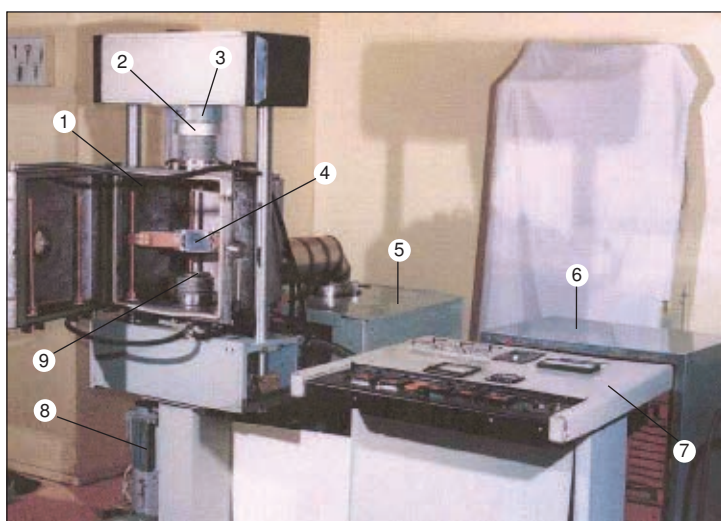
Установка СДВУ–100 для диффузионной сварки: 1 — модуль рабочей вакуумной камеры; 2 — силоизмерительное устройство; 3 — система нагружения; 4 — нагреватель; 5 — модуль вакуумирования; 6 — трансформатор; 7 — модуль управления; 8 — двигатель постоянного тока; 9 — рабочий стол
